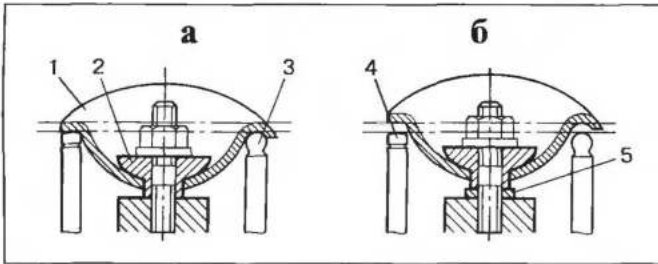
Устранение "зажатия" клапана: а — исходное состояние — клапан "зажат", плунжер гидротолкателя на опоре; б — освобождение клапана (и гидротолкателя) с помощью шайбы, подкладываемой под опору коромысла; 1 — коромысло; 2 — опора коромысла; 3 — штанга; 4 — стержень клапана; 5 — дополнительная шайба
